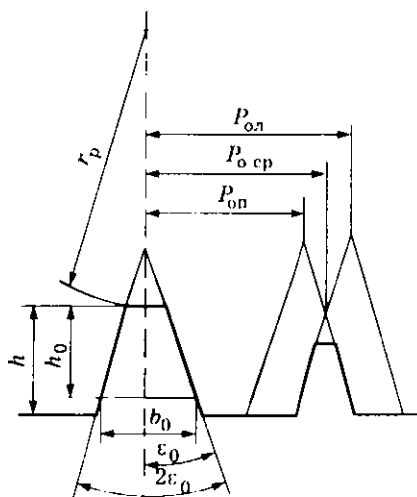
Размеры зубьев улиточной фрезы в осевом сечении
